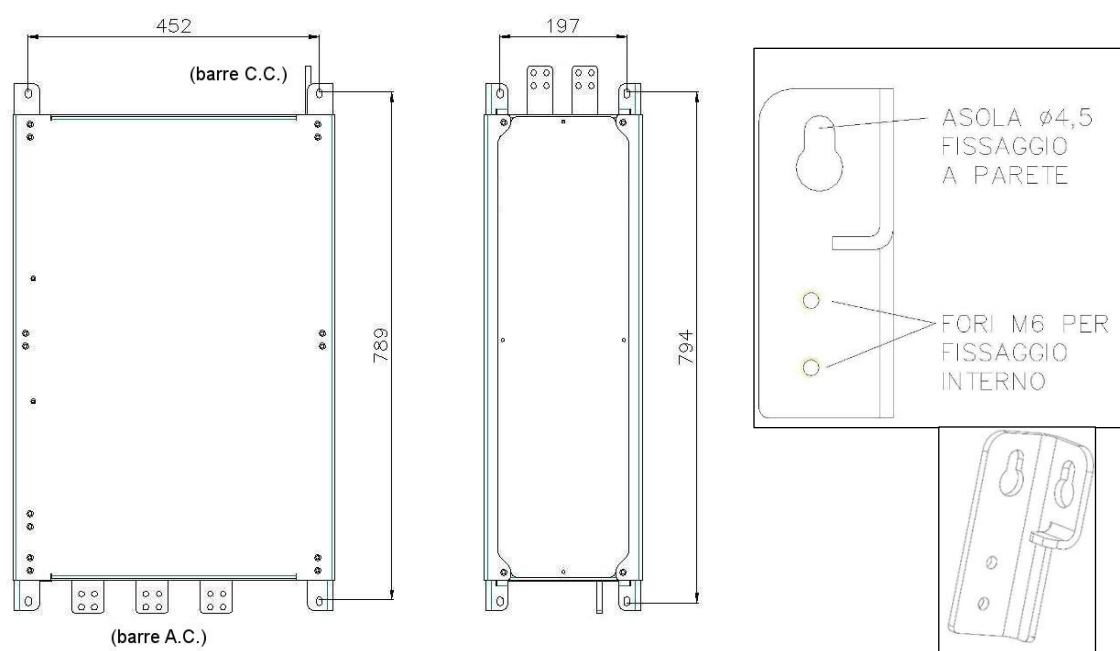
Dimensioni di fissaggio RPU 750-1000-1250 A
